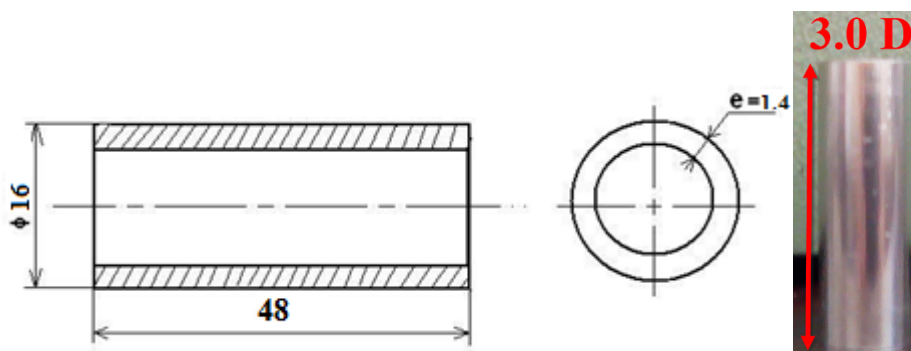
Dimensions de l'éprouvette étudiée .
